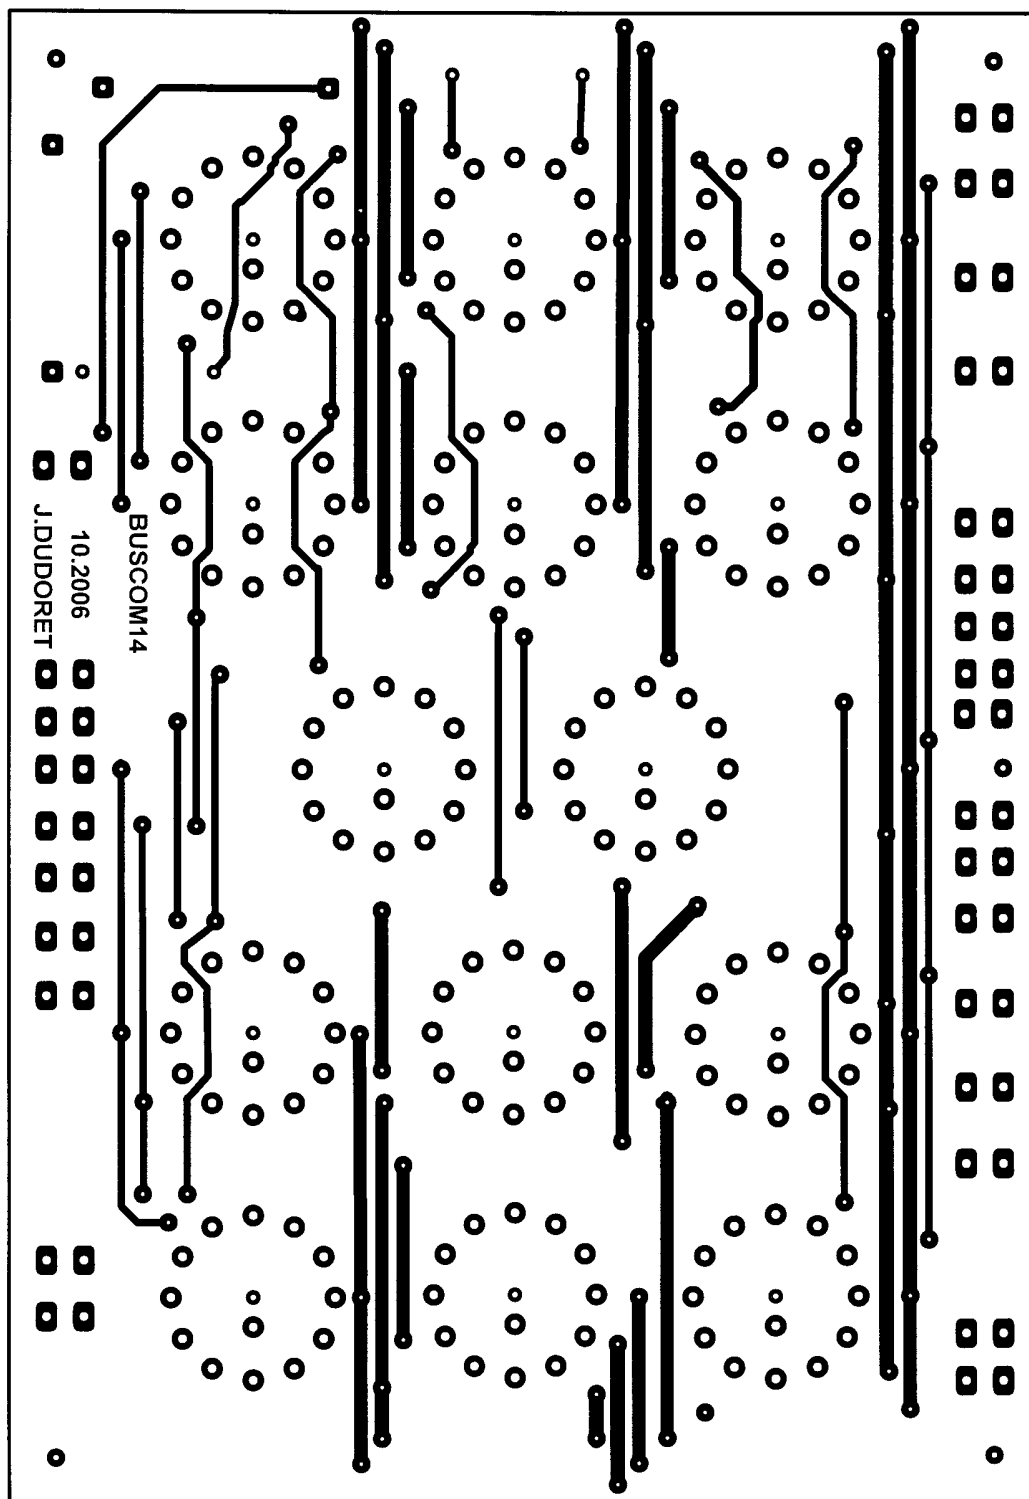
Circuit imprimé bloc de combinaison coté soudures.
